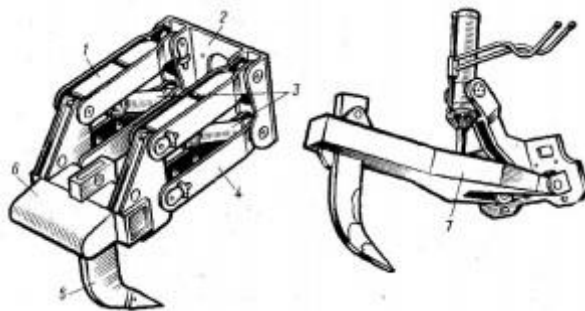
Навесное рыхлительное оборудование: 1 — верхняя тяга; 2 — опорная рама; 3 — гидроцилиндры заглубления; 4 нижняя рама; 5 — зуб; 6 — рабочая балка; 7— рама рыхлителя.
